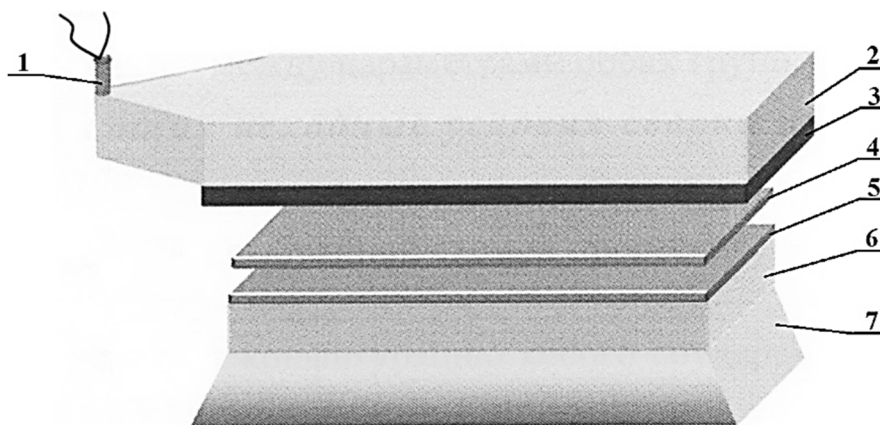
Схема сварки композиционного материала взрывом:
